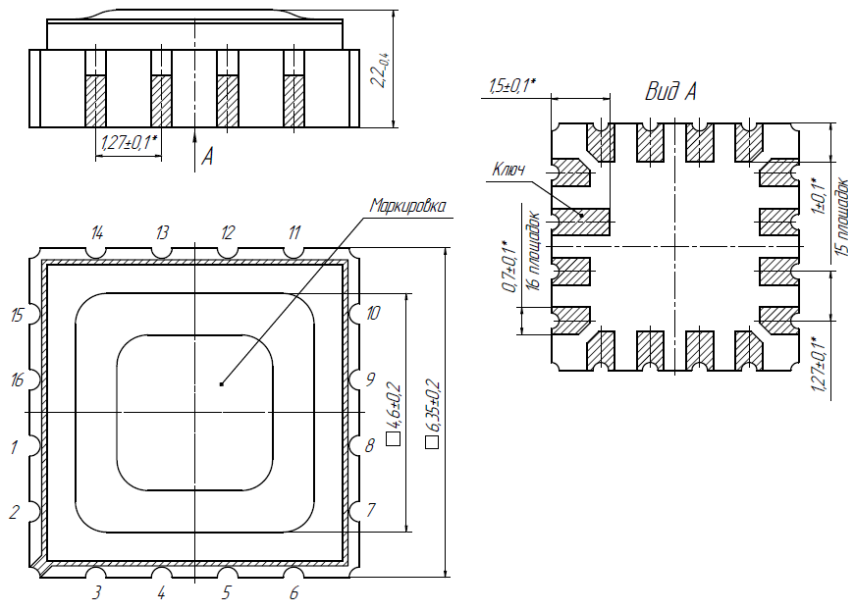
Внешний вид корпуса 5130.16-АНЗ
